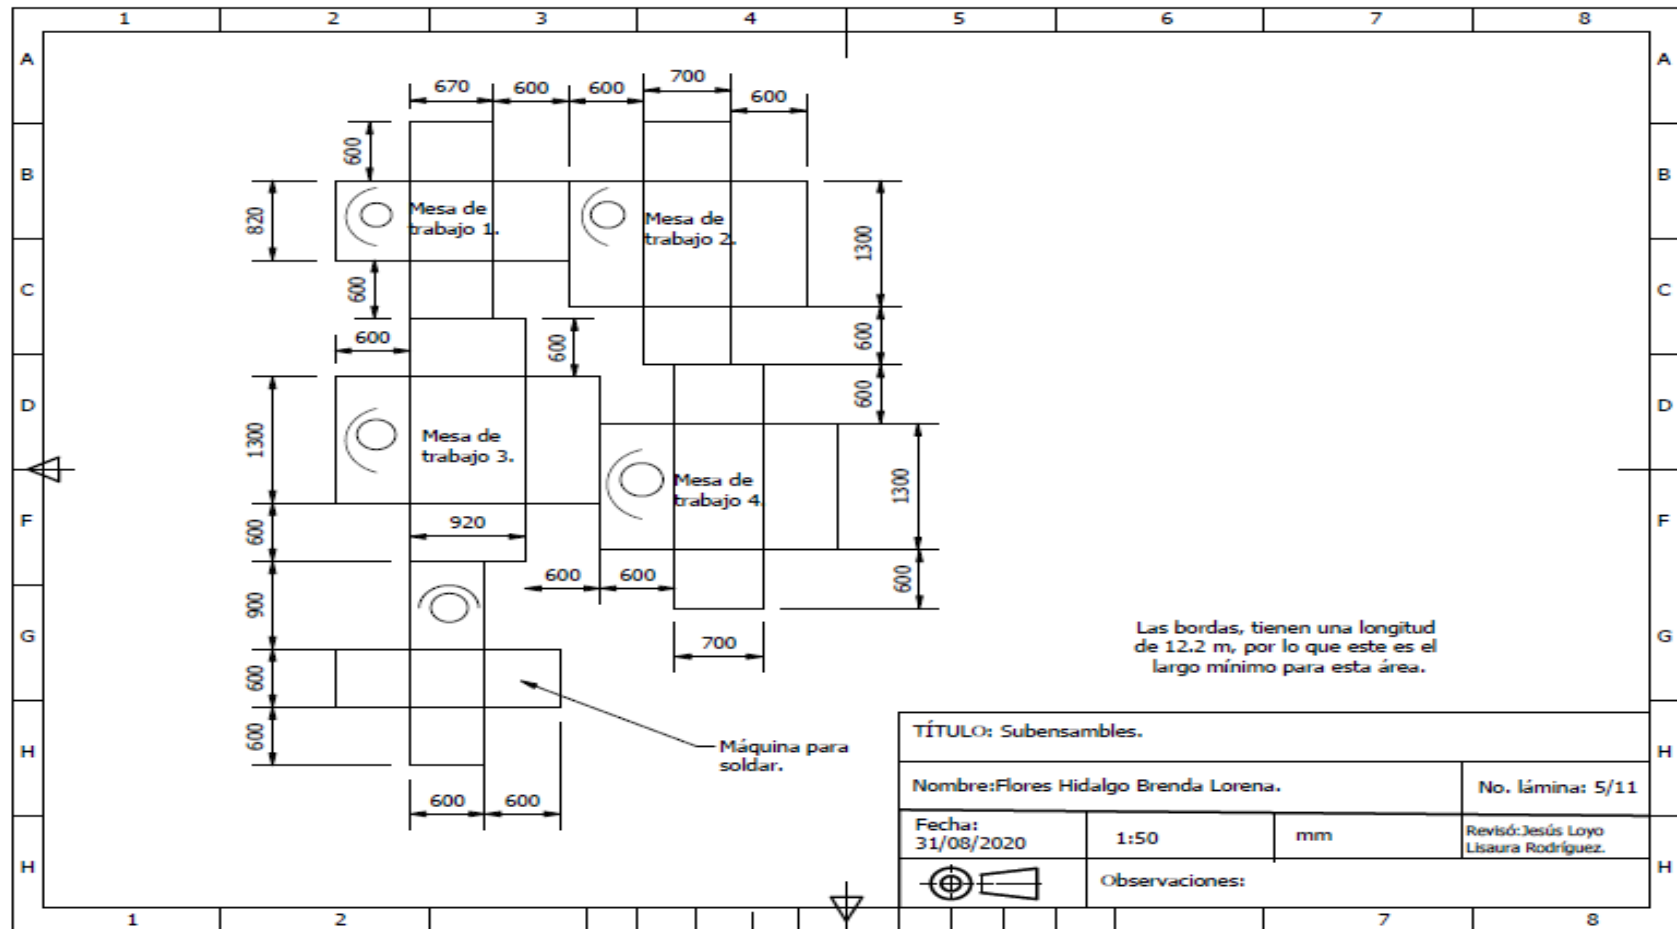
Plano del espacio requerido para la estación de subensambles. Fuente: Elaboración propia.
